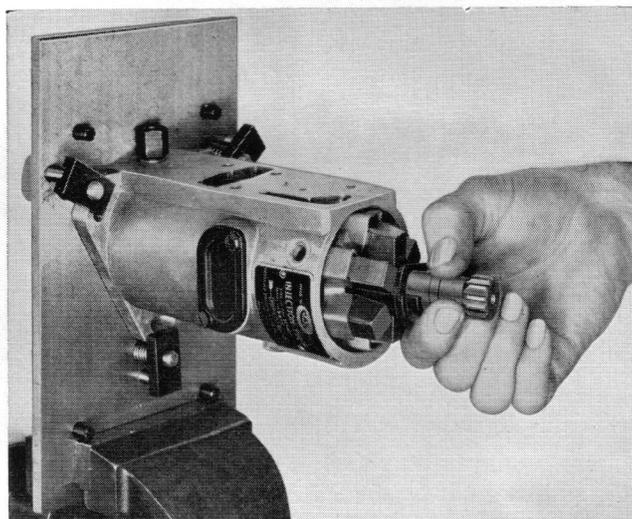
Démontage de l'ensemble des masselottes et de l'arbre d'entraînement cannelé
